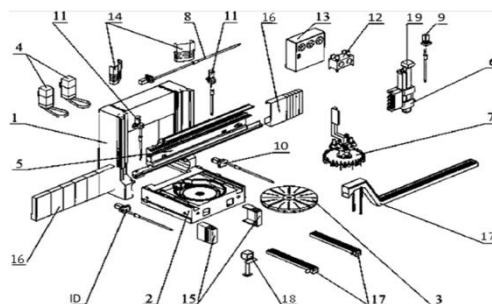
Схема расположения узлов токарно-карусельного станка
